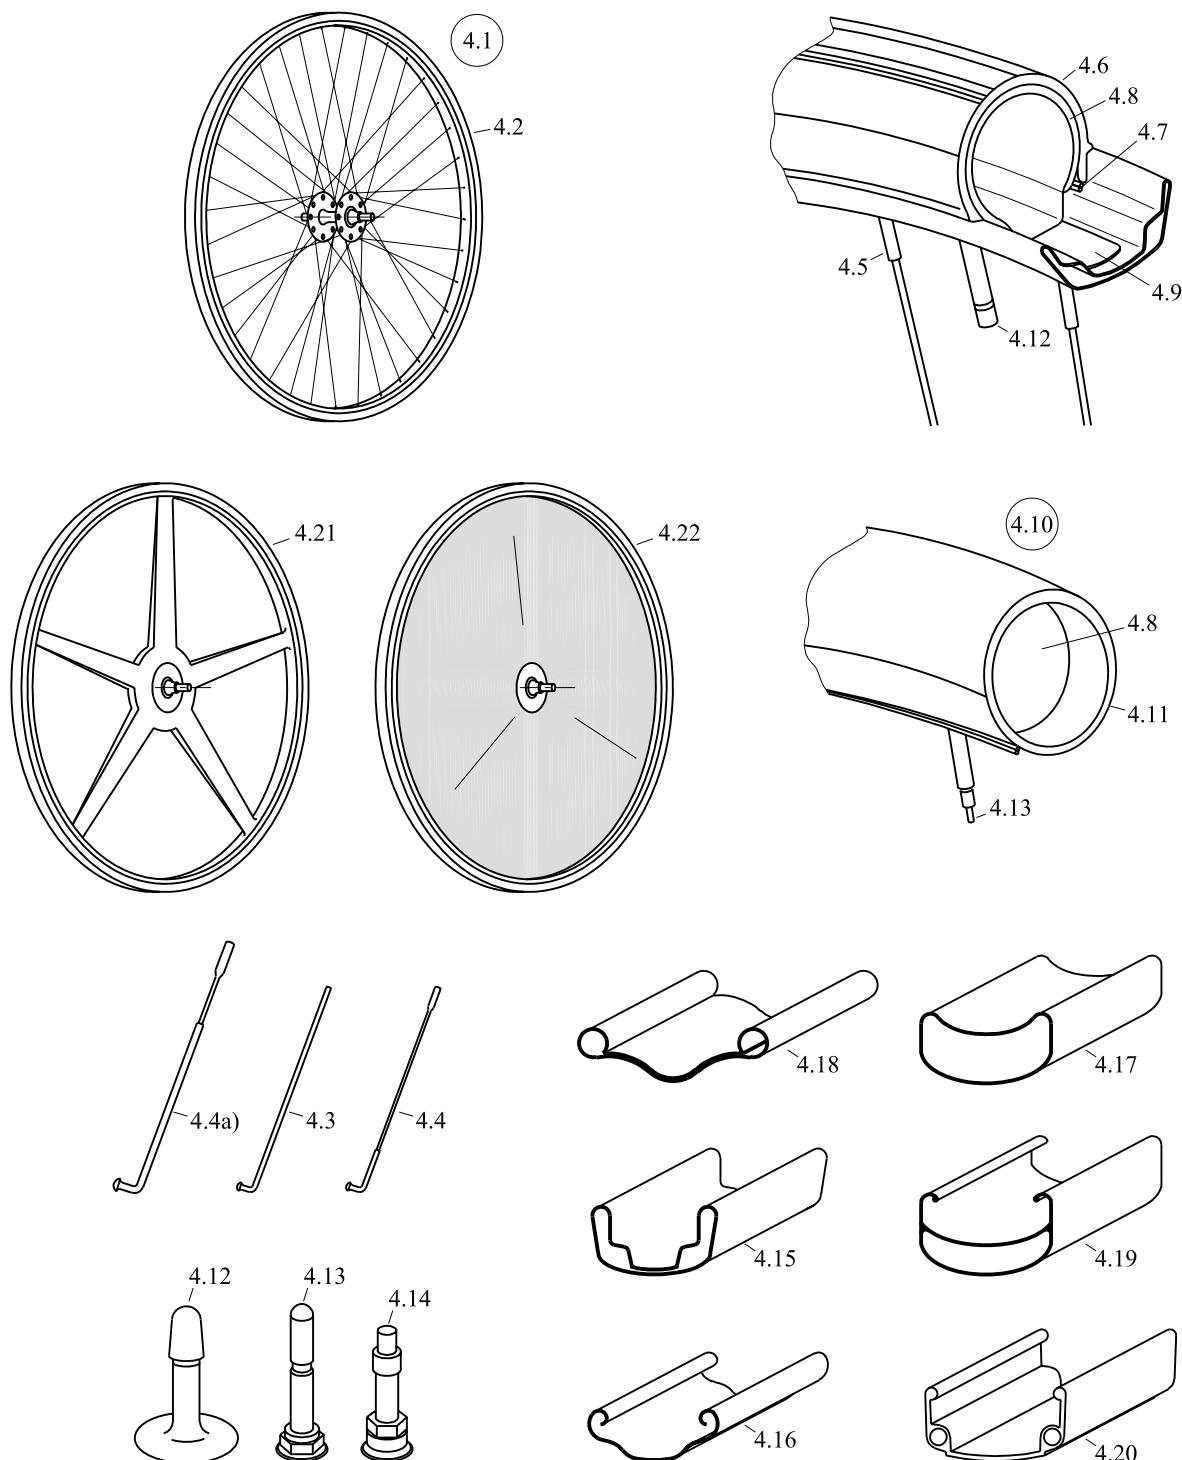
Roue / Wheel / Laufrad / Ruota / Wiel
